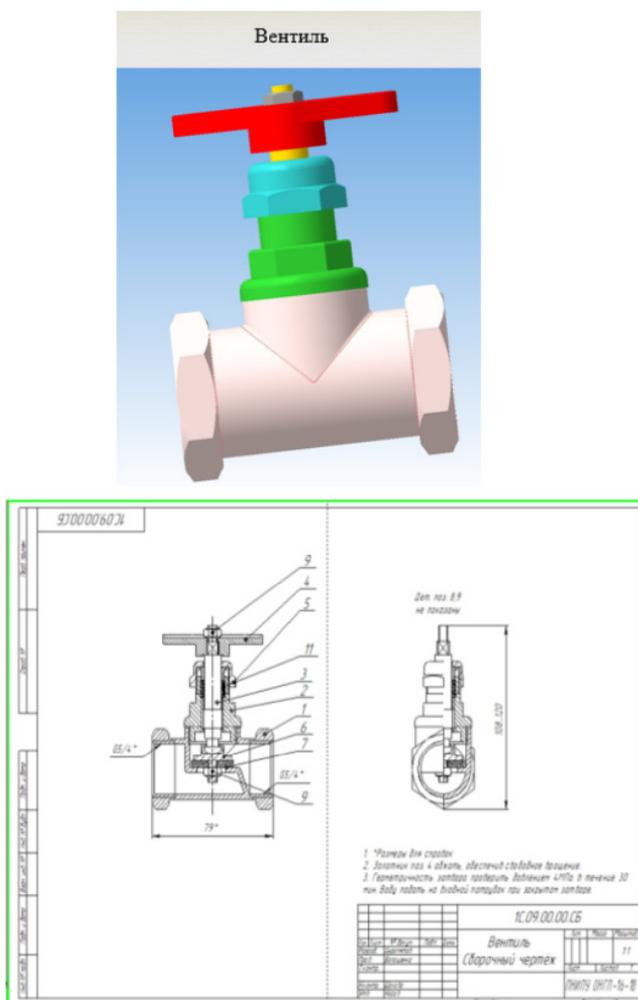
3D-модель и ассоциативный чертёж сборочной единицы
